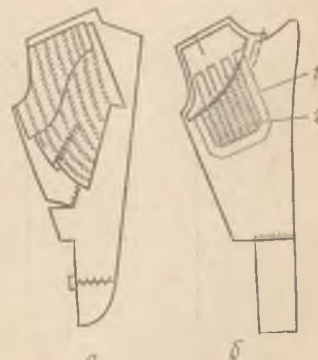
Обработка бортовой прокладки ниточным креплением
